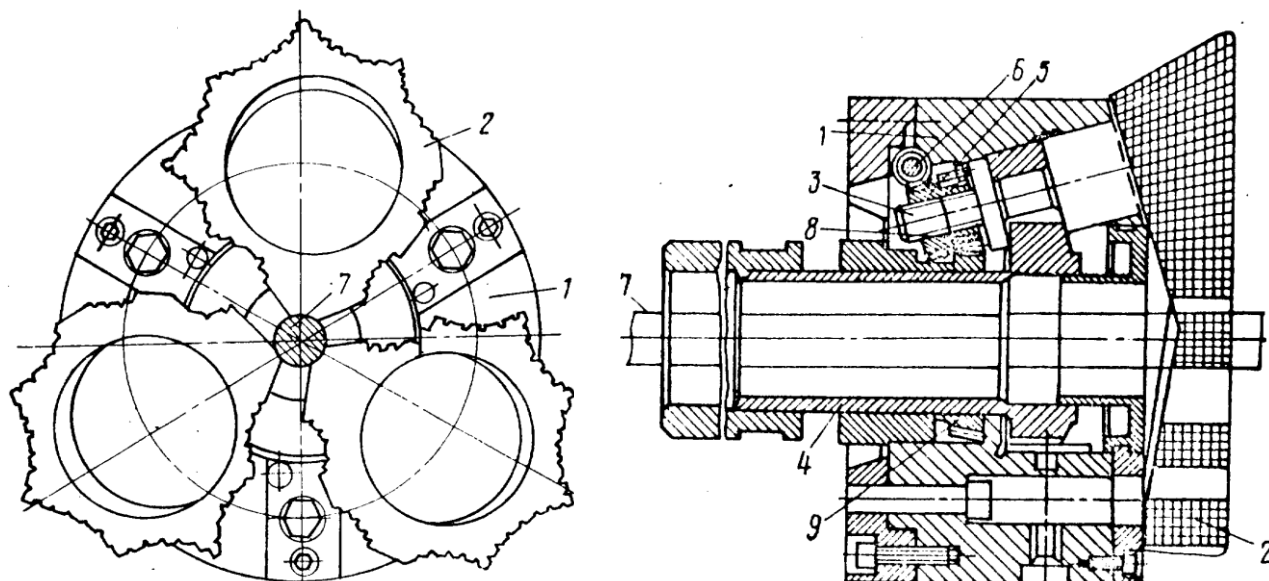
Швидкопереналагоджувальний токарний патрон плунжерного типу з одночасним позиціонуванням багатопрофільних затискних елементів
